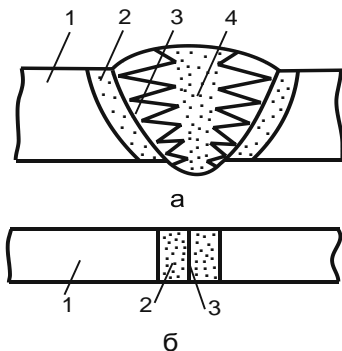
Схеми зварних з'єднань: зварювання плавленням (а); зварювання тиском (б): 1 – зварюваний метал; 2 – зона з'єднання; 3 – зона сплавлення (термомеханічного впливу); 4 – зварювальний шов
